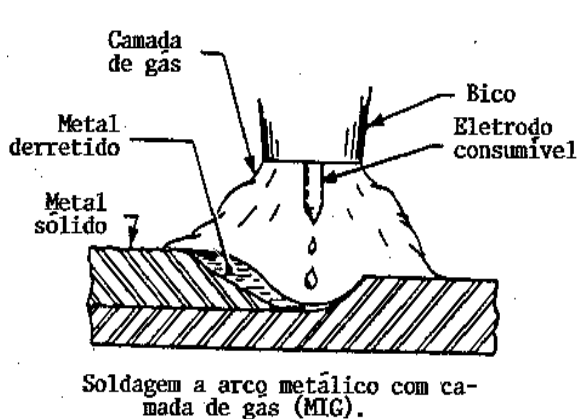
(A) Processos de soldagem a arco com camada de gás.
